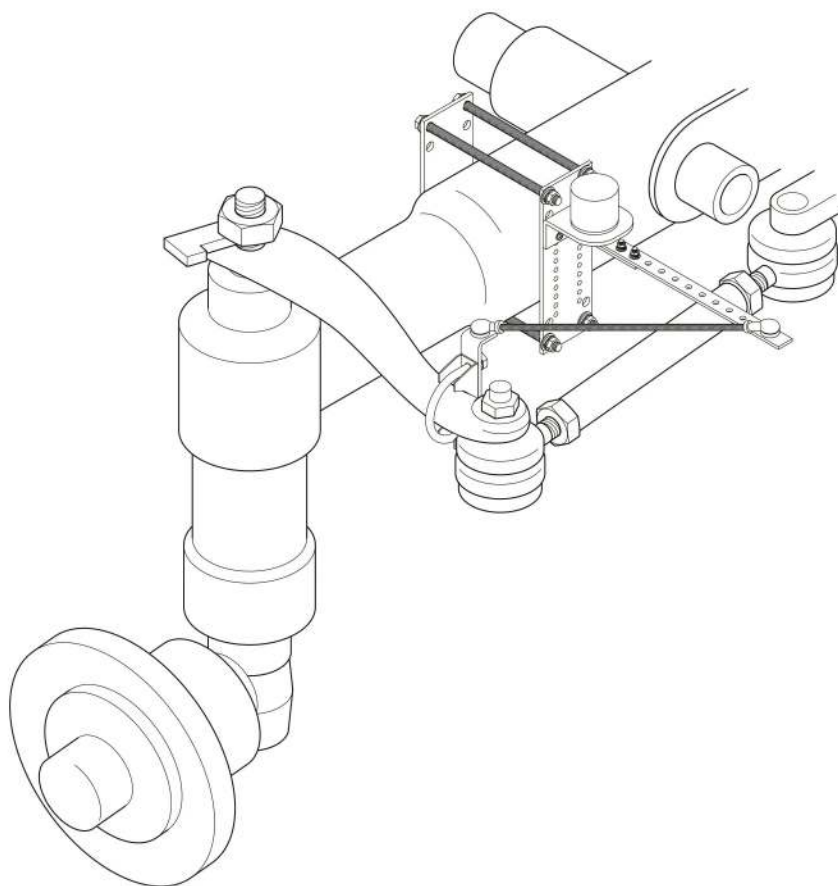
Установленное крепление датчика угла поворота на рулевую тягу в сборе
